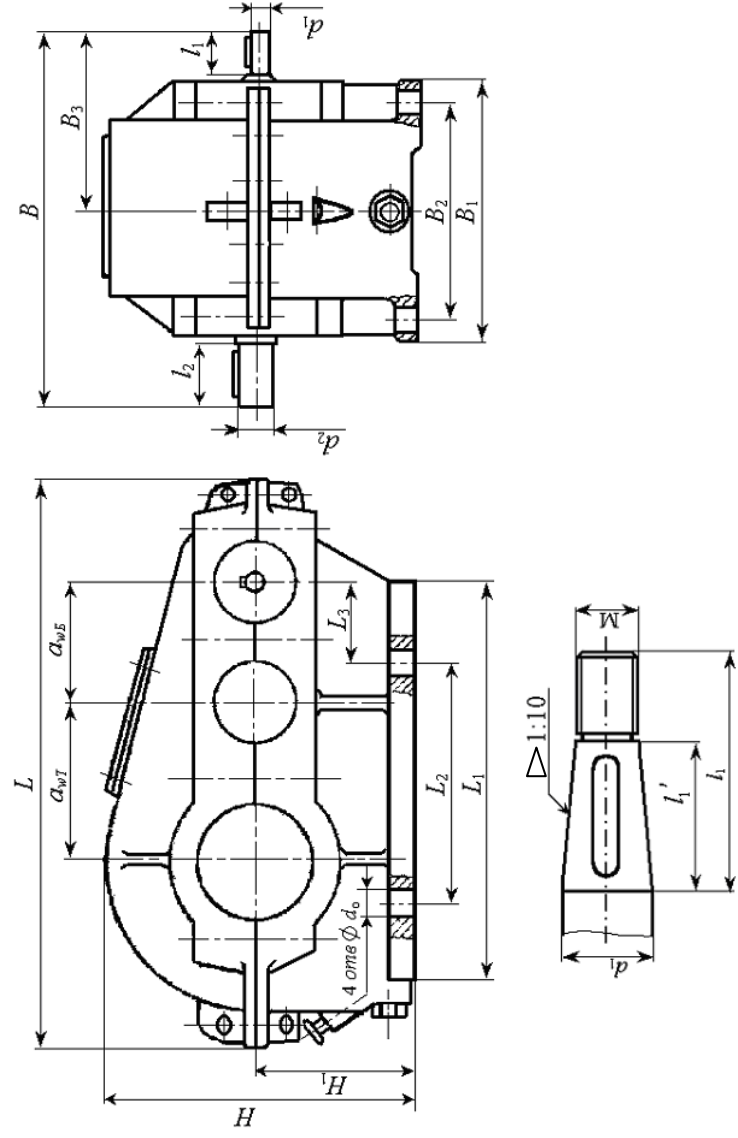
Габаритные и присоединительные размеры редуктора
